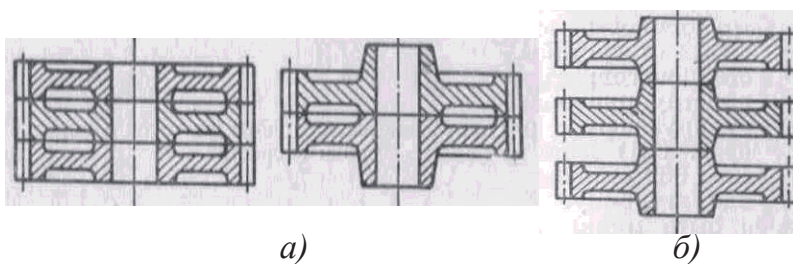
Два варианта расположения обрабатываемых поверхностей на торце зубчатых колес: *a* – технологичное; *б* – нетехнологичное
